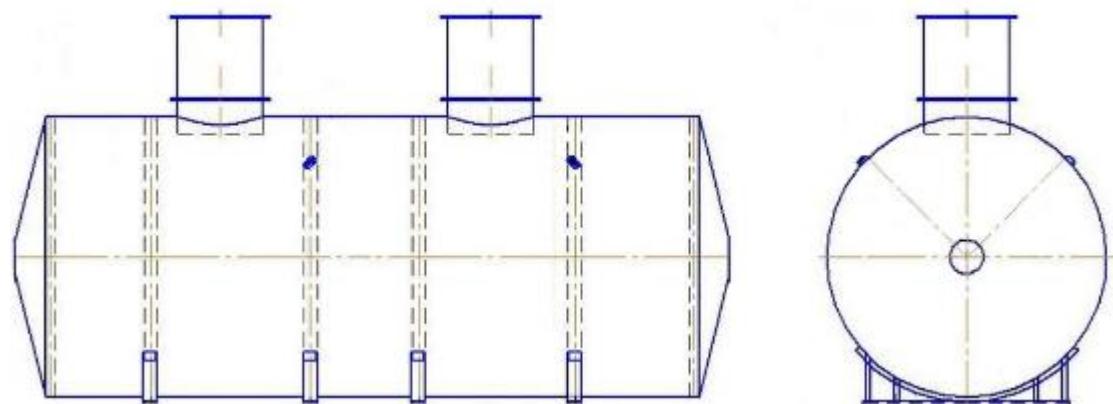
Эскиз общего вида резервуара РГС-50
